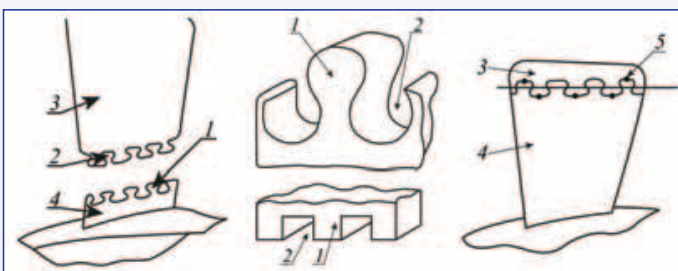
Схема ремонта крыльчаток ротора: 1 - профильные шипы; 2 - профильные пазы; 3 - сменная лопатка; 4 - основание лопатки; 5 - прихватки
